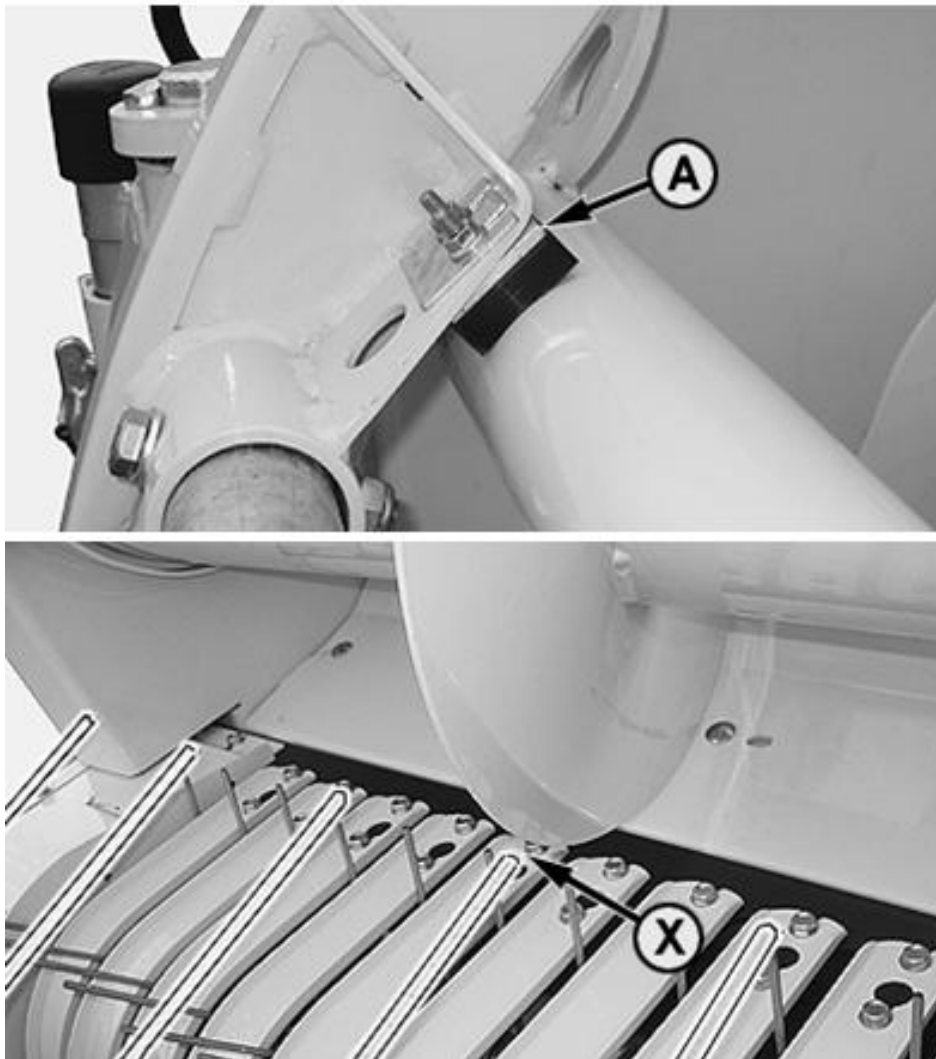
Регулировка рабочей высоты пальцевого прижима нормализатора
